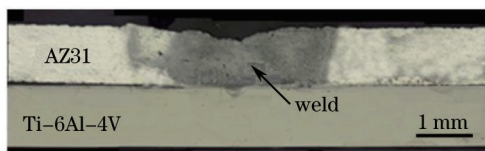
典型镁/钛激光熔钎焊接头截面形貌
